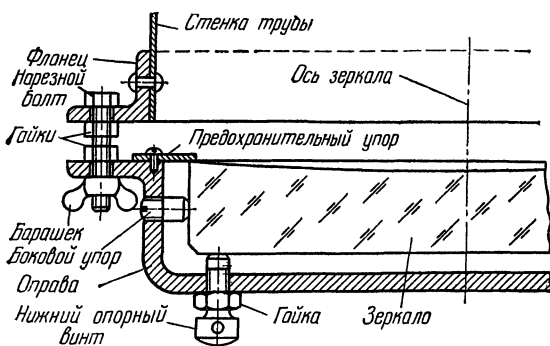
Устройство и крепление более совершенной металлической оправы главного зеркала.
